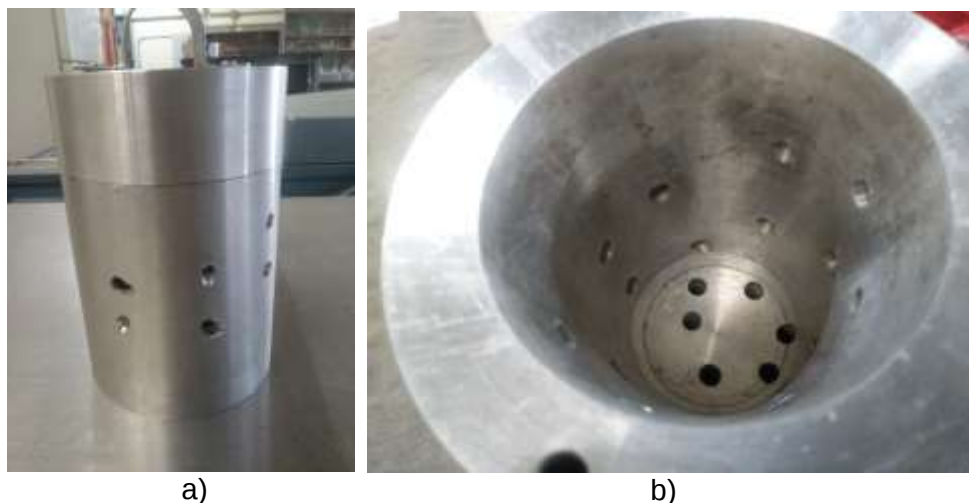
Molde final obtenido a) Vista completa del molde ensamblado, b) Vista superior de lado A del molde.
